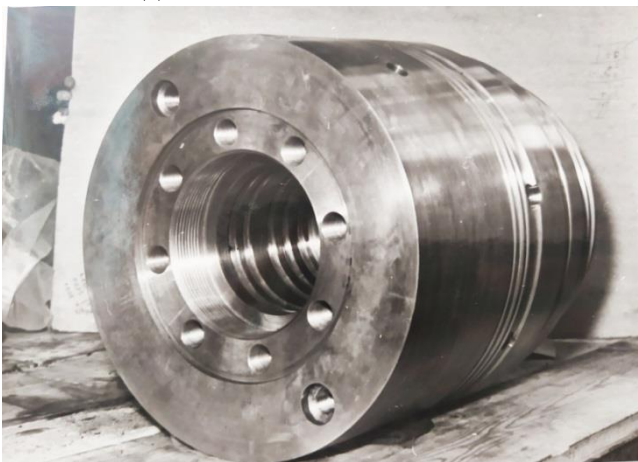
Торцева кришка зовнішнього корпусу
